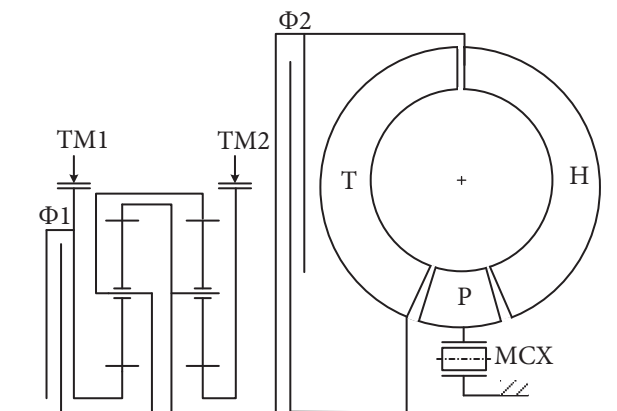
Первый вариант кинематической схемы ГМП с регулируемым согласующим редуктором
